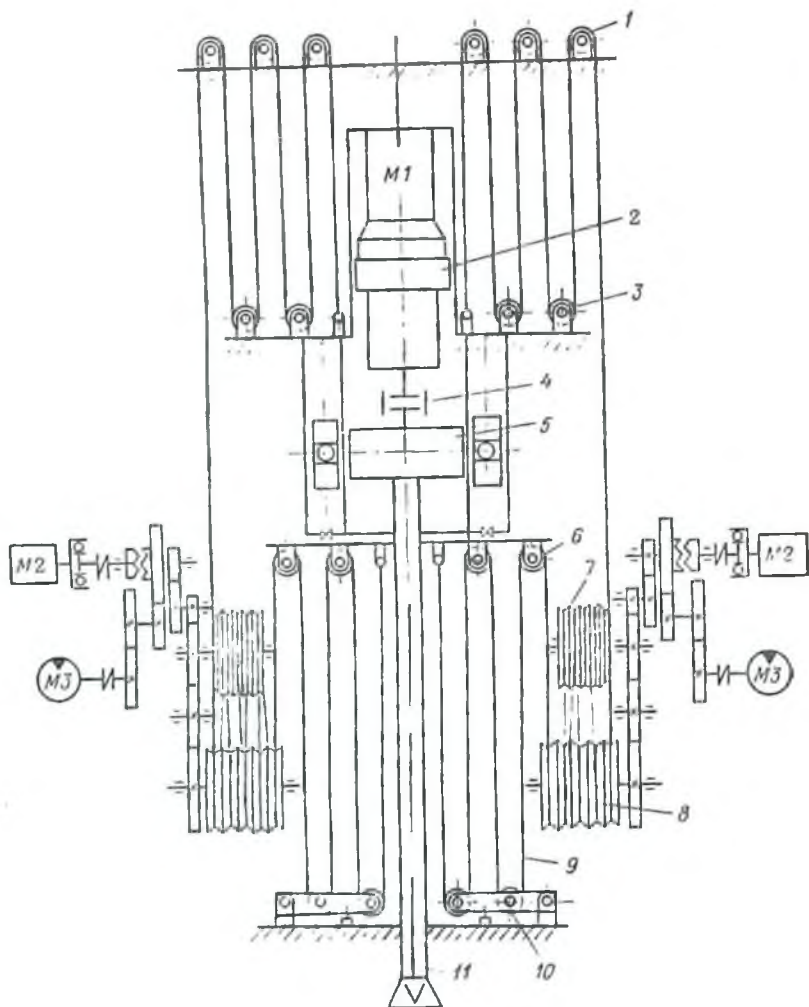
Кинематическая схема вращательно-подающего механизма с канатно-полиспастной системой подачи станка шарошечного бурения СБШ-320-36
